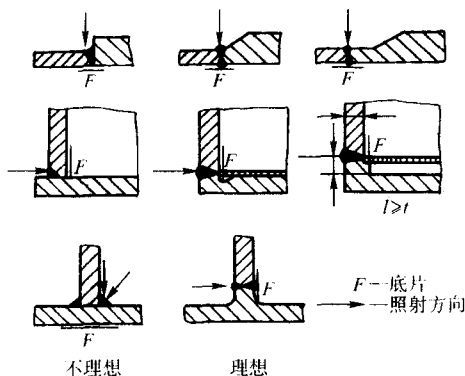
适于射线探伤的焊接结构设计
